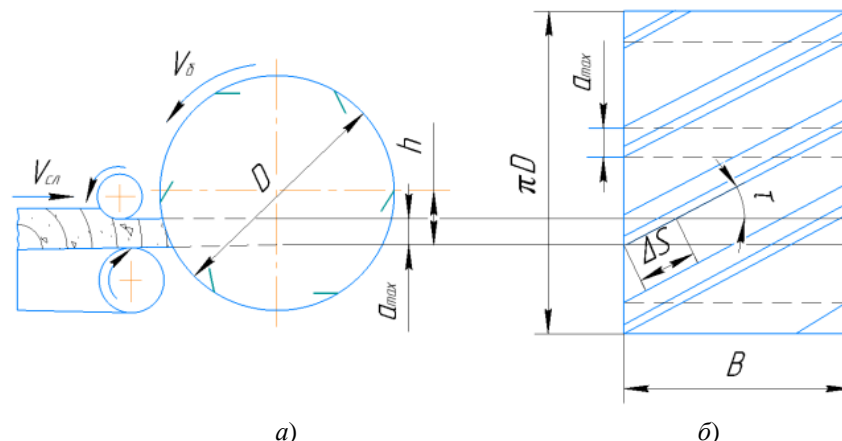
Схема режущего аппарата барабанного типа (а) и развертка ножевого барабана (б)
